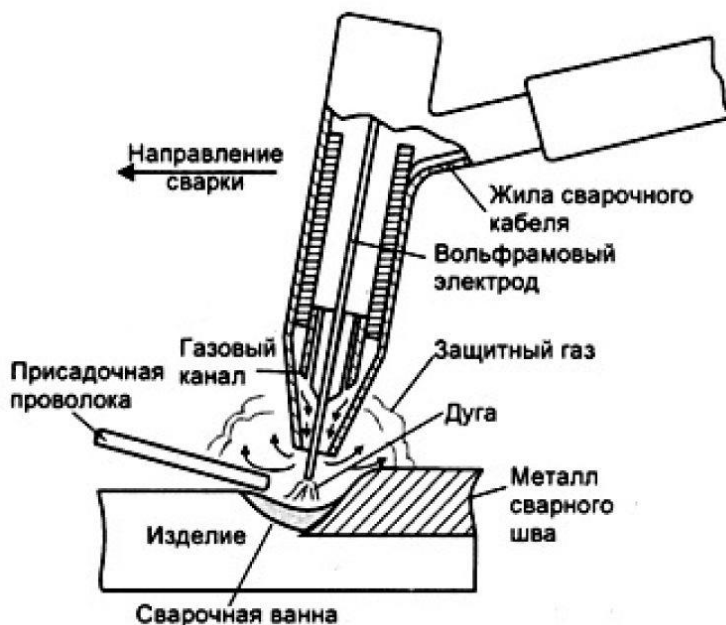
Схема осуществления сварки неплавящимся электродом в среде защитного газа
